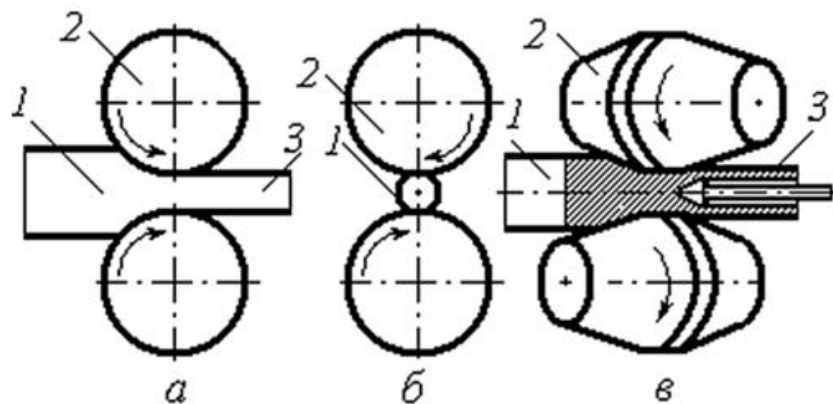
Схеми прокатки: а - поздовжньої; б - поперечної; в - поперечно-гвинтовий (прокатка труби); 1 - заготовка; 2 - валки; 3 – виріб.
